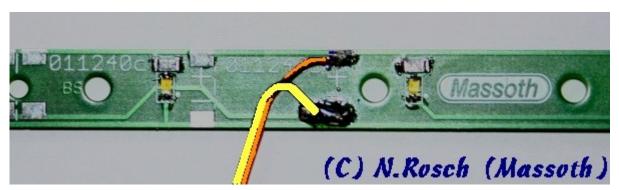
Massoth Lichtleiste mit Kabelanschluss
